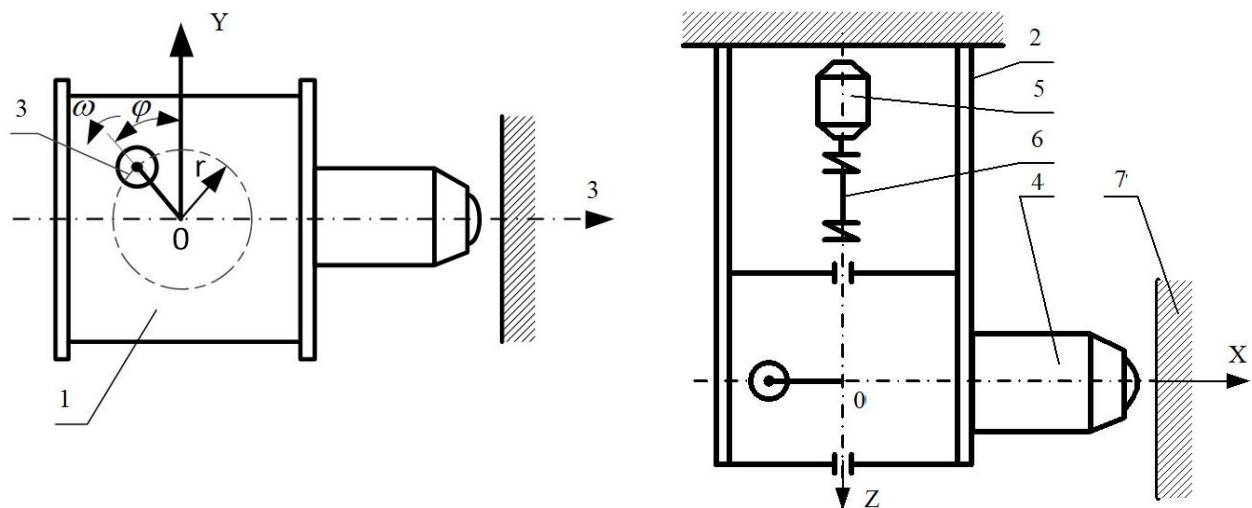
Схема эксцентрикового упрочнителя: 1 — корпус; 2 — плоская пружина; 3 — эксцентриковая масса; 4 — инструментальная головка; 5 — электродвигатель; 6 — гибкий вал; 7 — ограничитель (обрабатываемая деталь)
